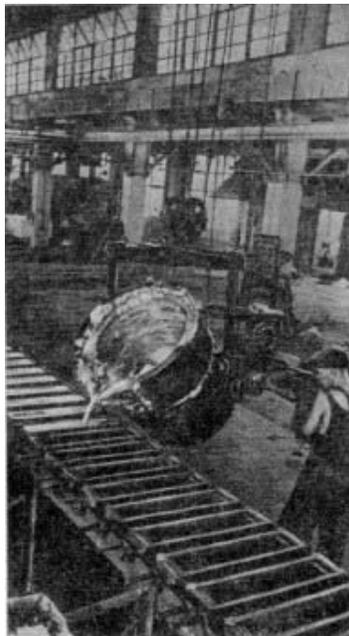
Vaciado en moldes del aluminio en un taller de fundición
